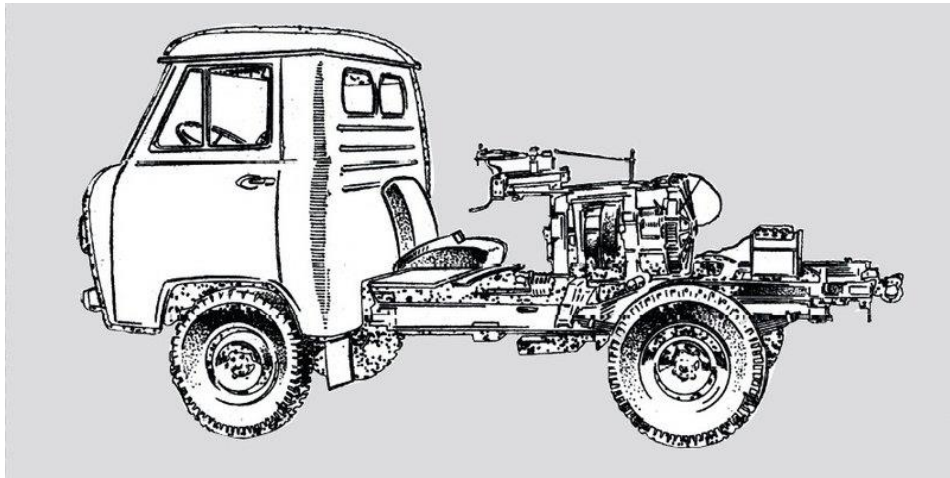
Механічний гібрид УАЗ-450Д [13].
